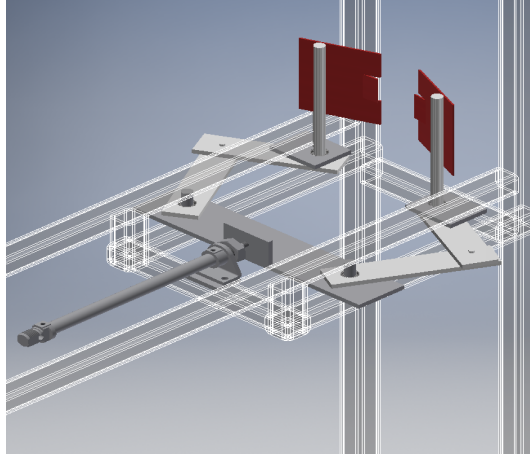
Modelo CAD de ensamblaje mecanismo de apertura.
